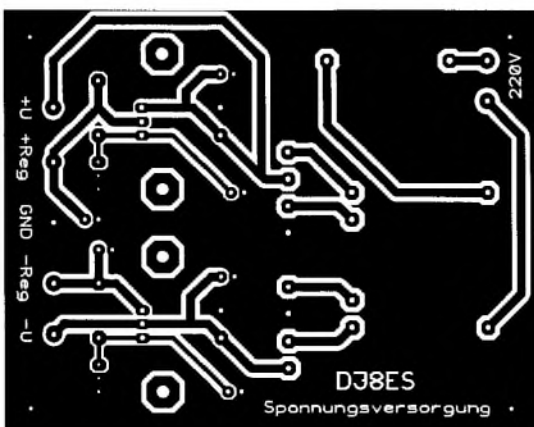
Platinenlayout zur Schaltung gemäß Bild 7
